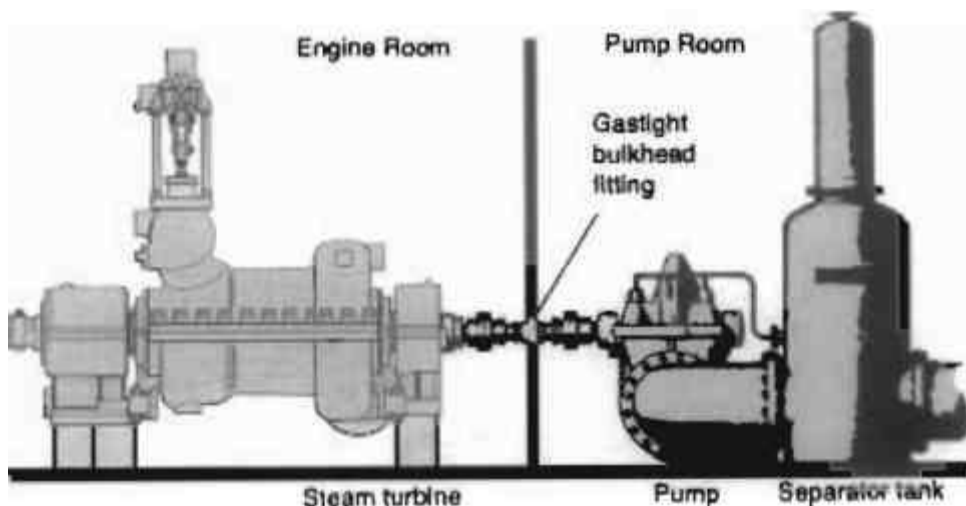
Ilustración de un conjunto de turbina y bomba de descarga de crudo en un petrolero. Fuente [49].
